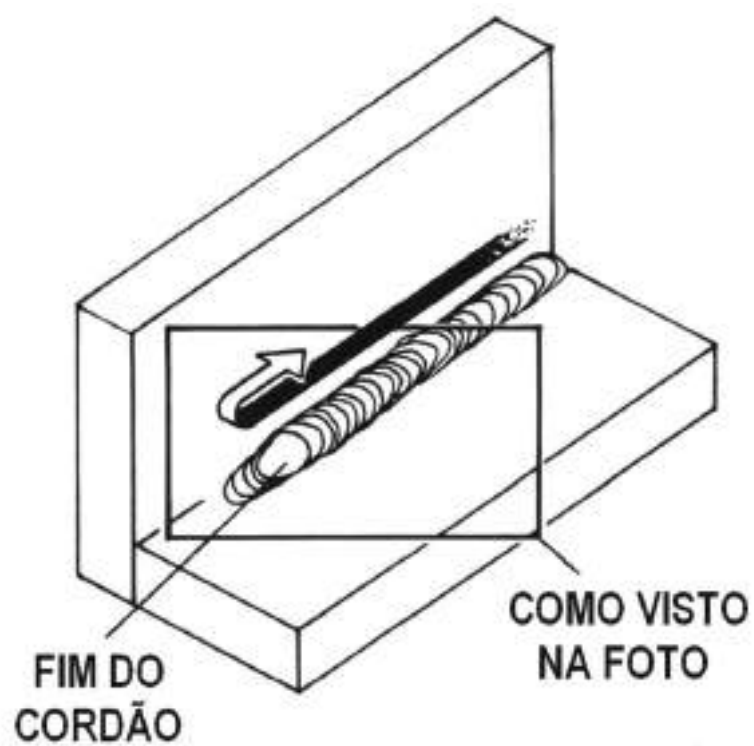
Técnica de enchimento de fissura de cratera.
